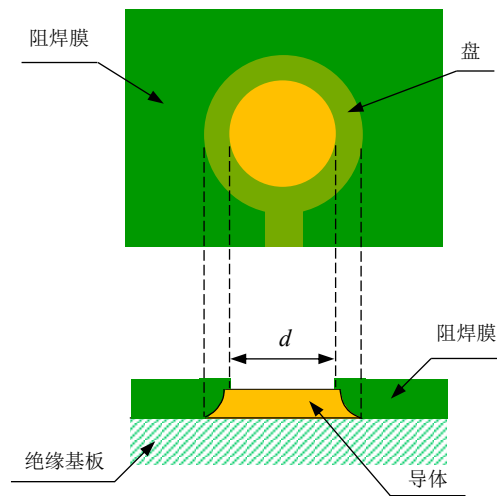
由阻焊膜开窗所界定的 BGA 盘径
